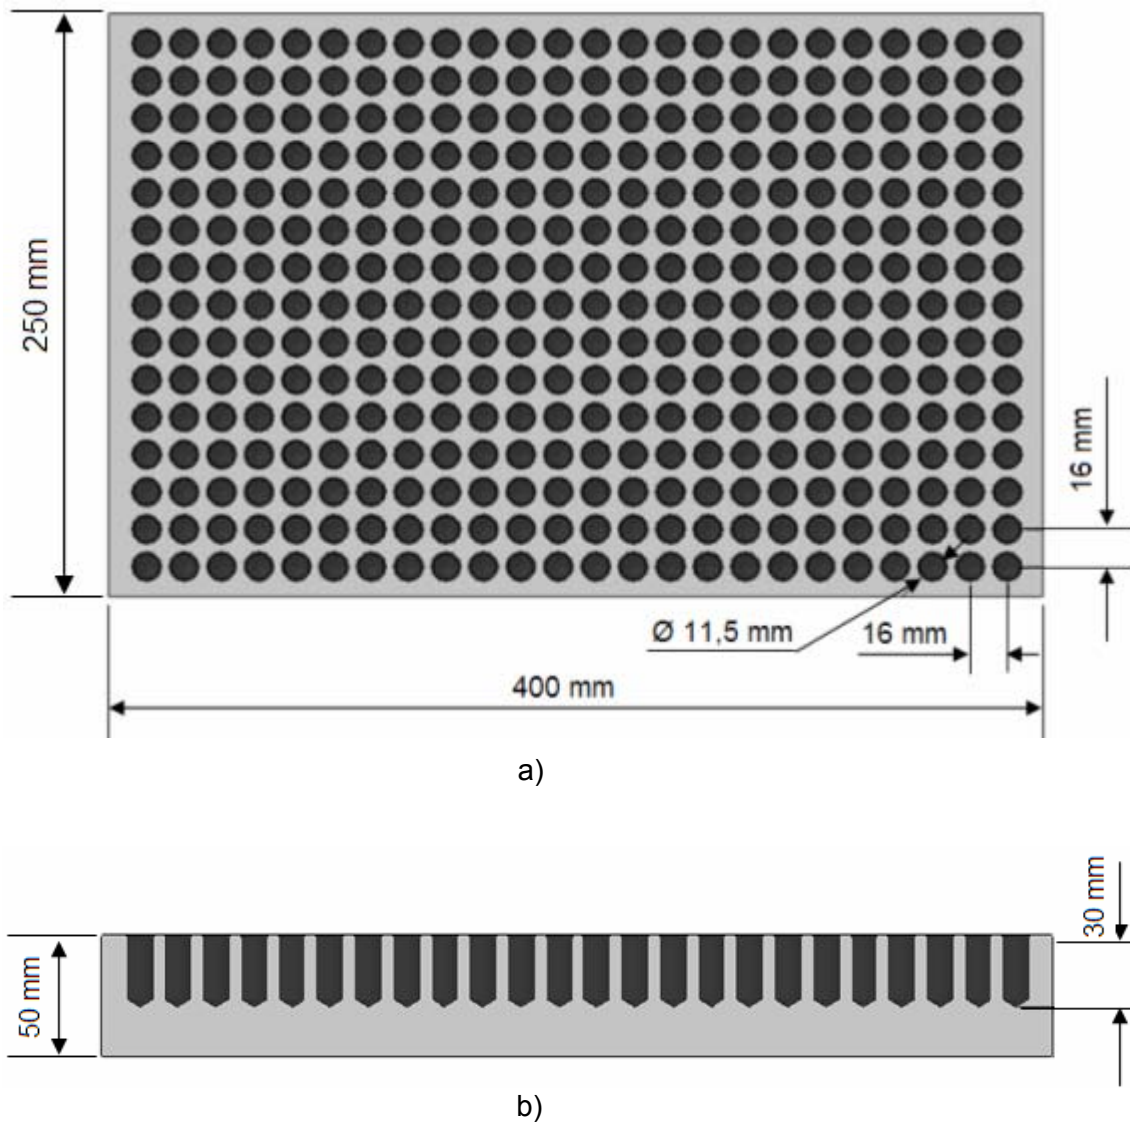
Desenho esquemático da placa de ferro fundido vermicular; a) vista superior da placa rosqueada; b) vista lateral do corpo de prova
